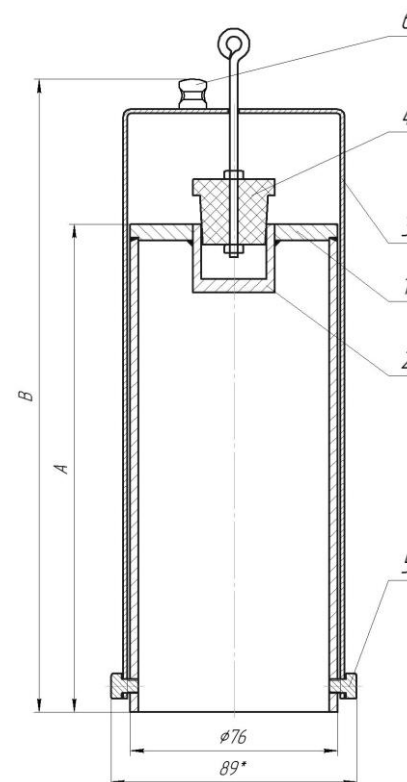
Пробоотборник ППН-750: 1 – корпус, 2 – глухое отверстие, 3 – рамка, 4 – пробка-фиксатор со штоком, 5 – винт установочный, 6 – бобышка.
